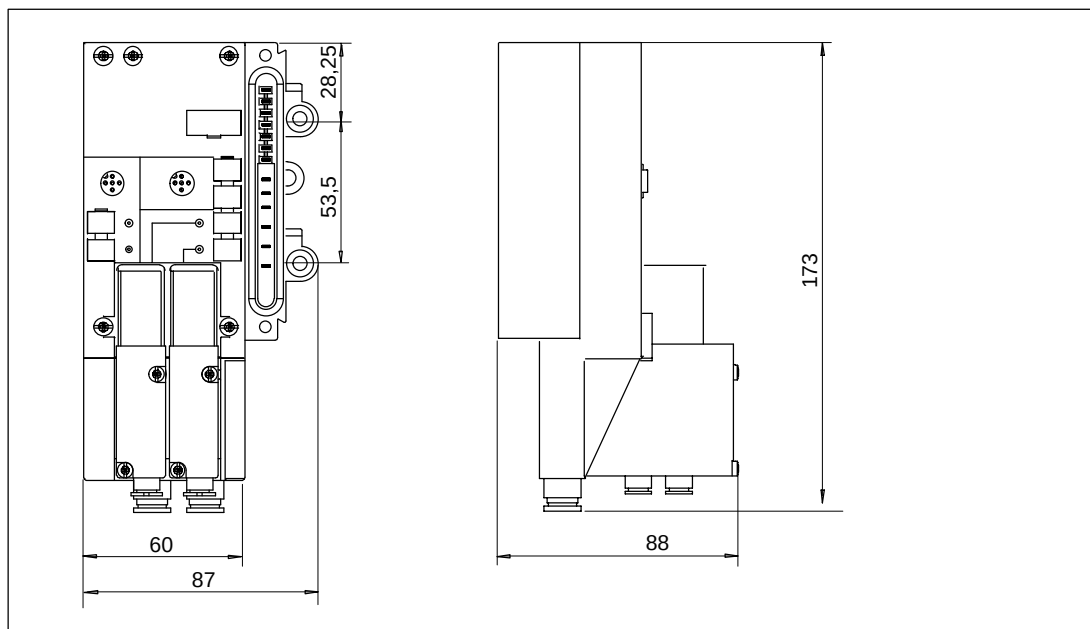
Disegno quotato Modulo Pneumatic Interface
